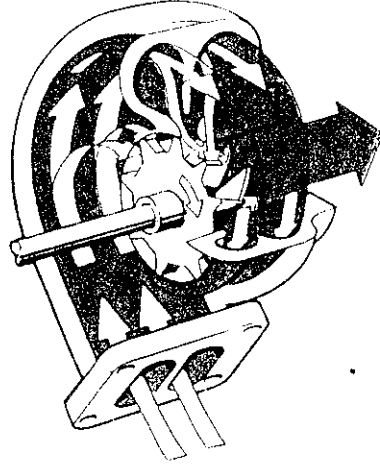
Diesel Motorlar İçin Dizayn Edilmiş Bir Turbo Şarj Grubu
